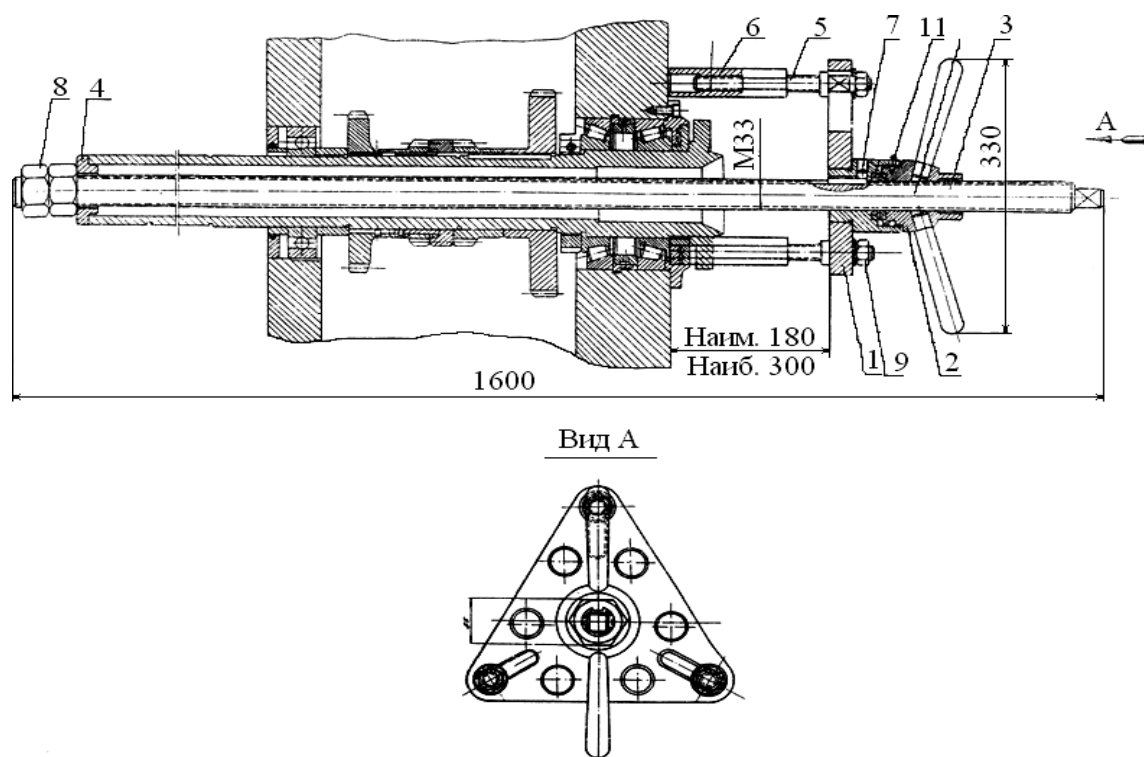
Приспособление для выпрессовки шпинделей токарных и револьверных станков СД 7911 – 4004
